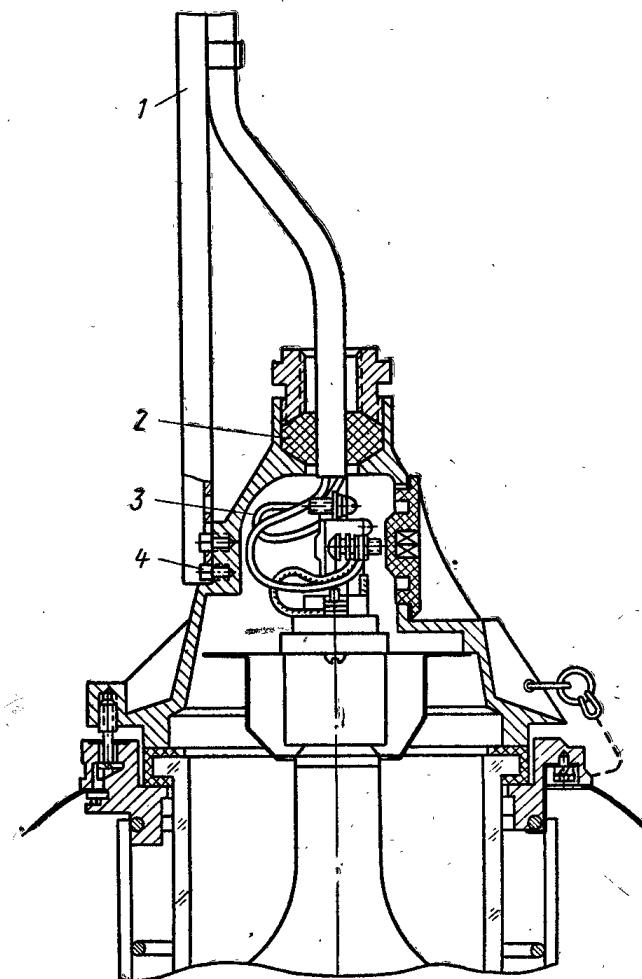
Ввод проводов во взрывозащищенный светильник Н45Н-150.
